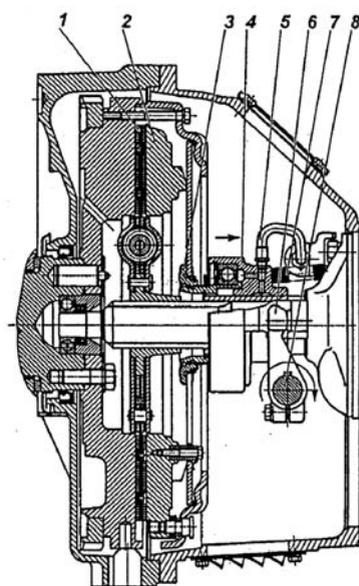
Сцепление модели ЯМЗ-182: 1 — ведомый диск; 2 — нажимной диск; 3 — упорное кольцо; 4 — муфта выключения сцепления; 5 — шланг смазки; 6 — вилка выключения сцепления; 7 — оттяжная пружина; 8 — валик вилки выключения сцепления
